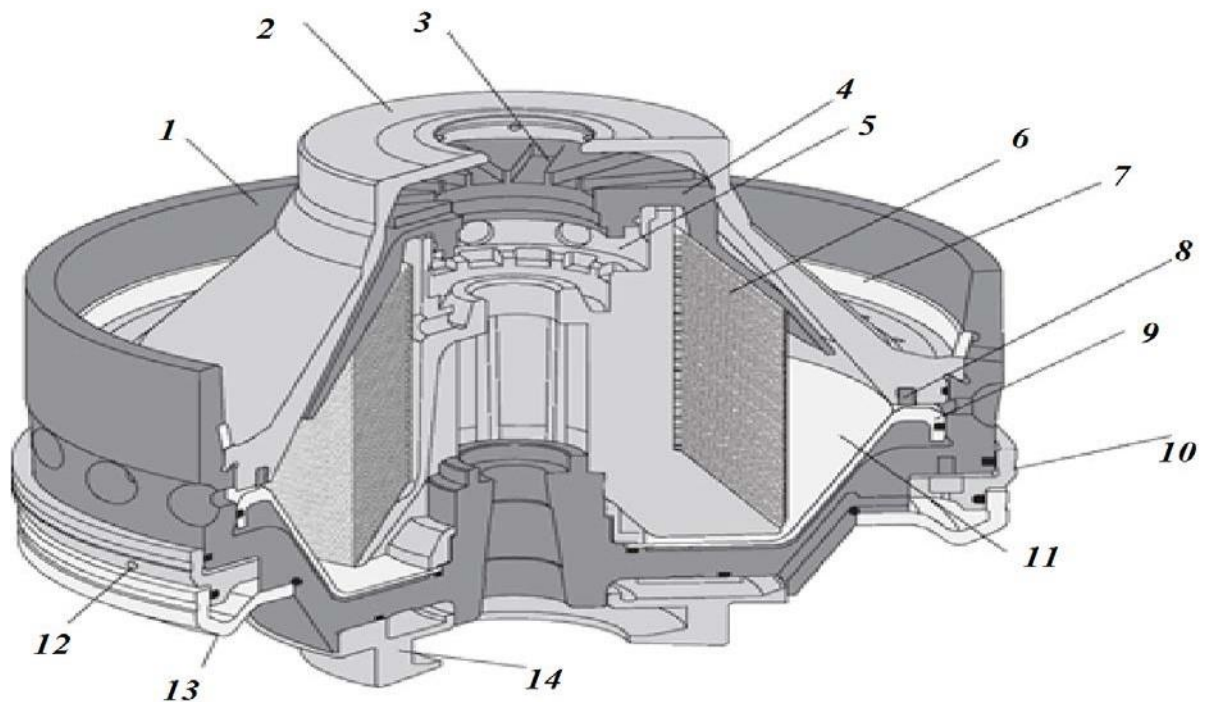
Барабан сепаратору: 1 - корпус барабану; 2 - ковпак барабана; 3 - водяна напірна камера; 4 - верхня тарілка; 5 - напірна камера; 6 - пакет тарілок; 7 - замкове кільце; 8 - кільце ущільнювача; 9 - розвантажувальний золотник; 10 - робочий золотник, 11 - зона осаду; 12 – форсунка; 13 – тримач; 14 – кільце для подачі води
